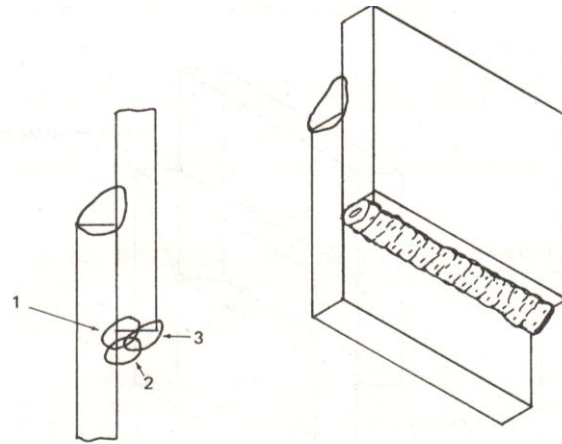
Girado del conjunto y aplicación de soldadura del lado opuesto.
